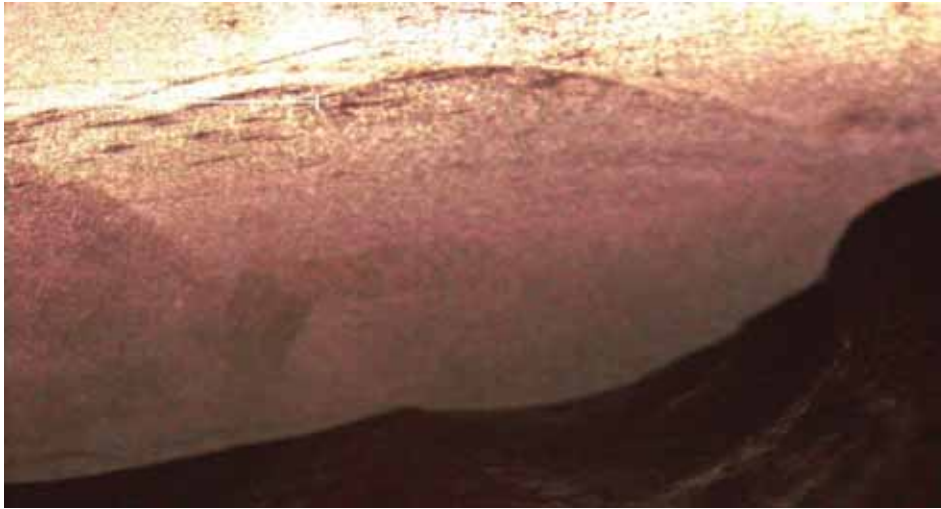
Detalhe do cordão de solda vista em microscópio da amostra 2
